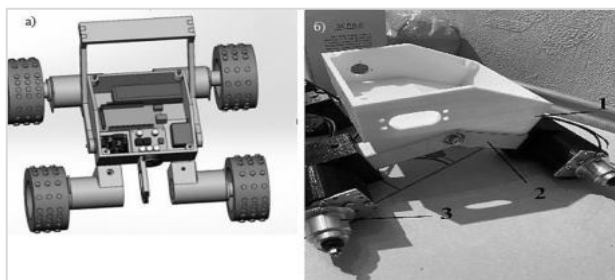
Внешний вид робота: 3D-модель (а), изготовленный корпус прототипа (б)
